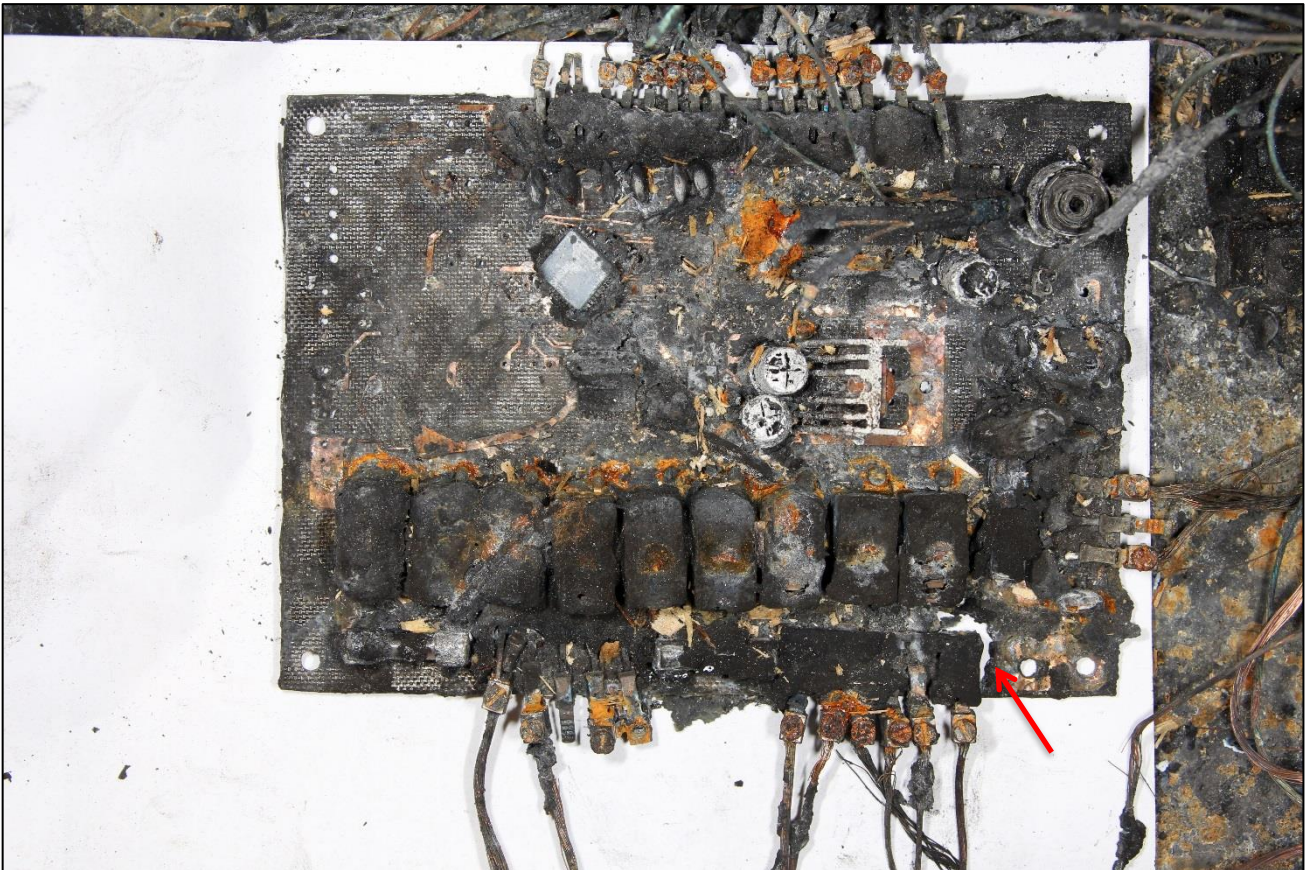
Styringsenheten etter demontering. Betegnelser på bakgrunnen viser hvor ledninger/kabler har vært tilsluttet.
